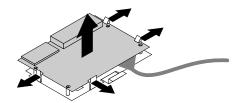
Remover o leitor de cartões do seu suporte de fixação
